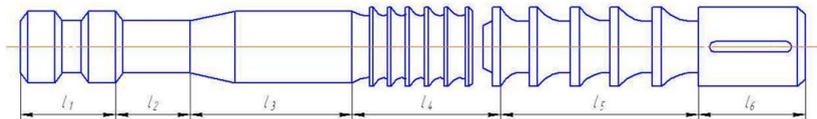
Конструкция протяжки для обработки внутренних поверхностей
